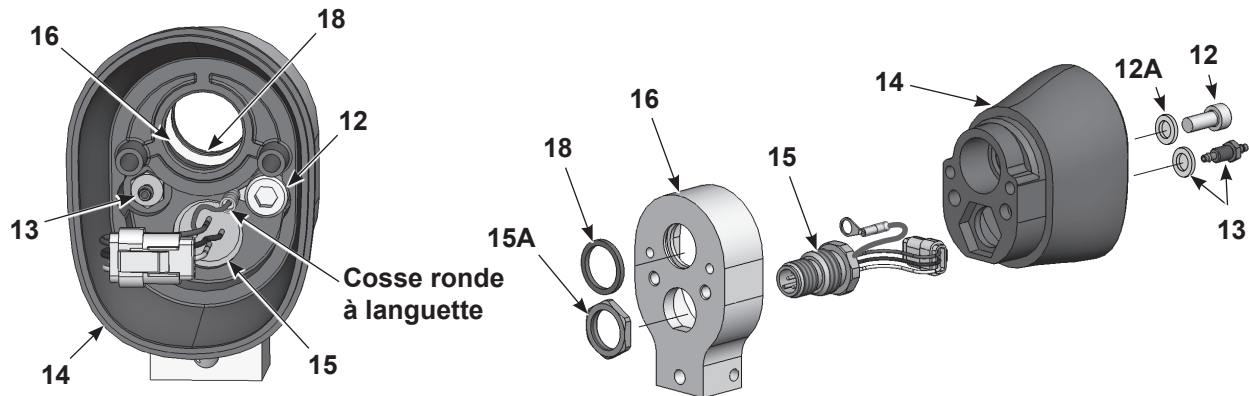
Démontage du pistolet à fixation sur barre 3 sur 3
